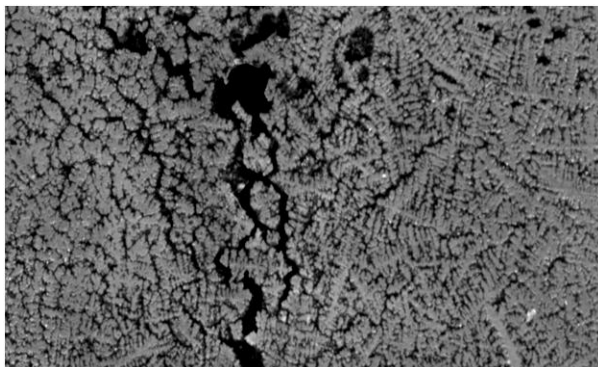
Макростроение горячей трещины в отливке корпуса дискового затвора (расположение трещины — радиусный переход проходного сечения к фланцу)
